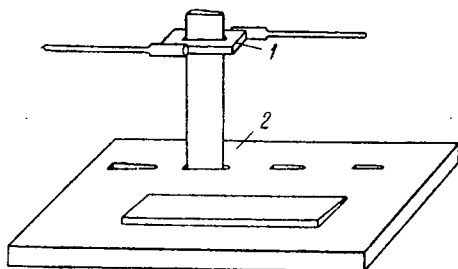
Приспособление для ручной рихтовки коллекторных пластин
